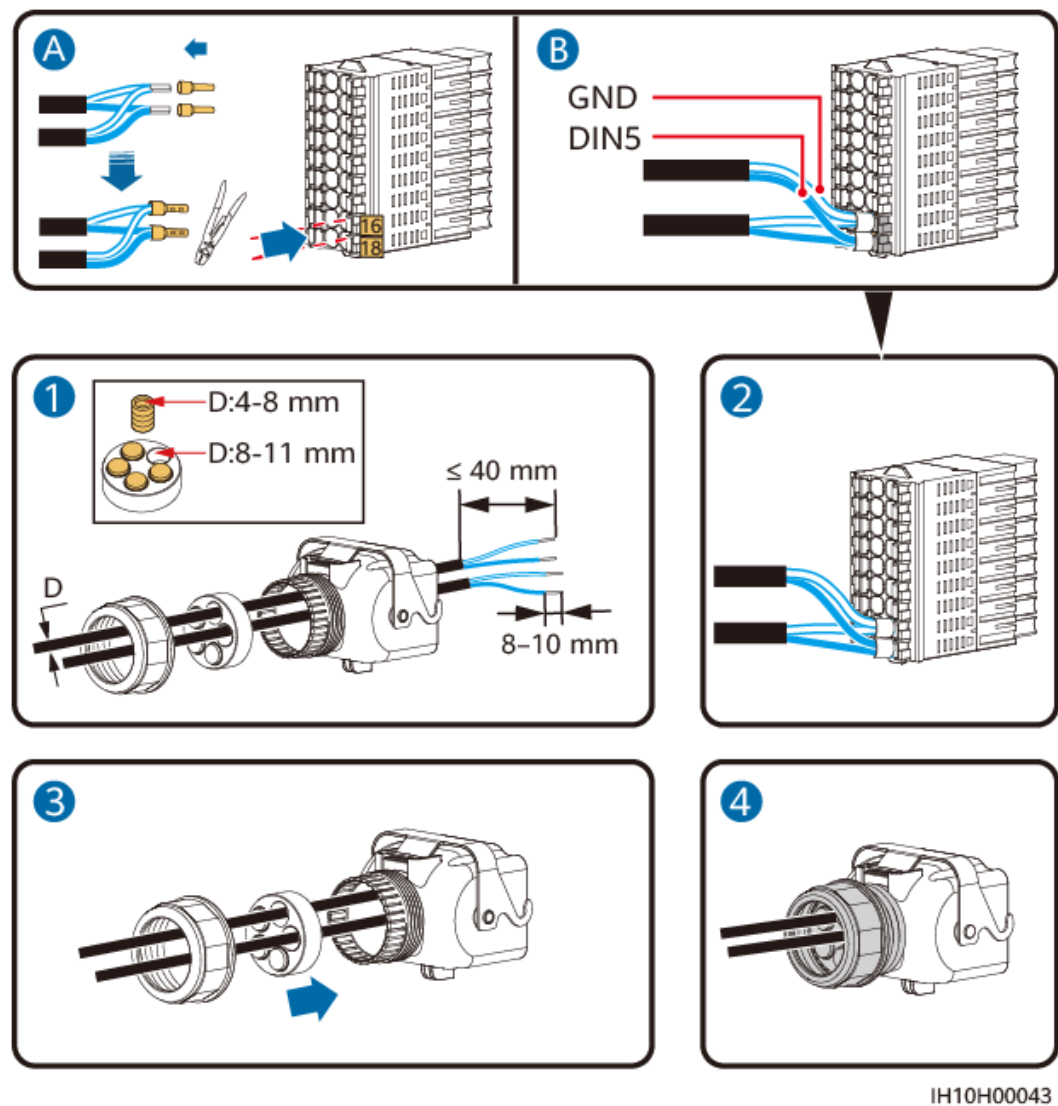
Collegamento di inverter in cascata all'interruttore di protezione rete e sistema
